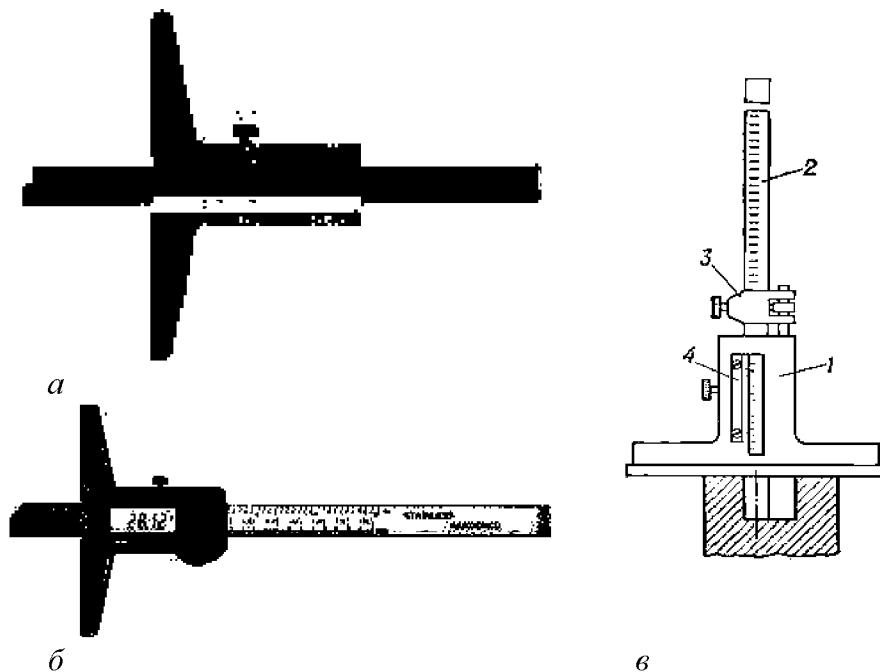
Штангенглубиномер: *а* – нониусный штангенглубиномер; *б* – штангенглубиномер с цифровой индикацией; *в* – схема измерения глубины:
